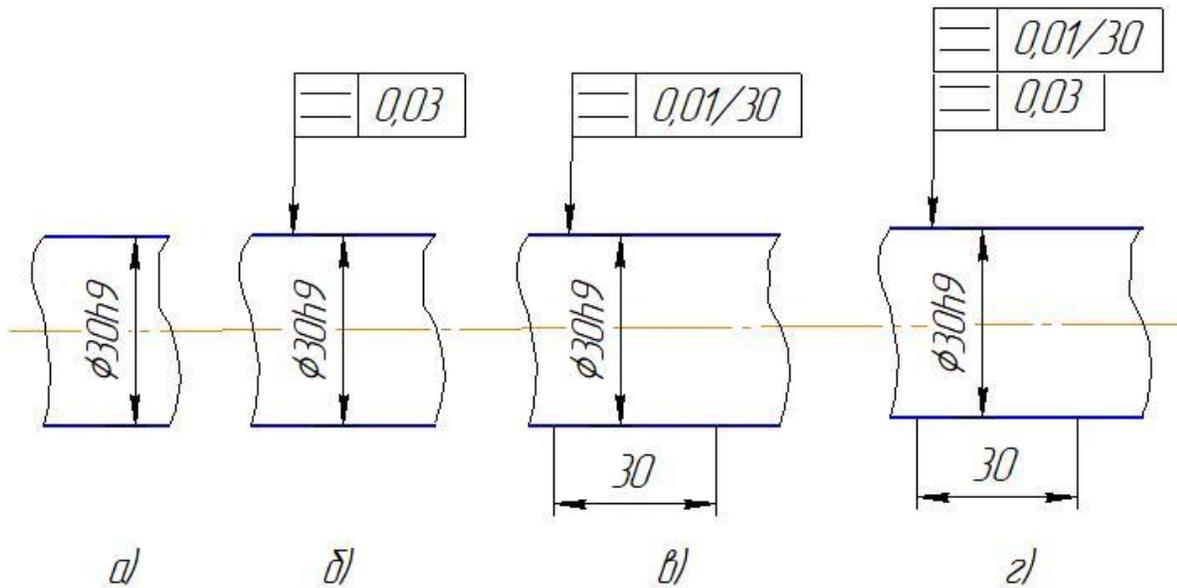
Позначення на кресленні відхилення профілю поздовжнього перерізу
